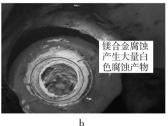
轮毂及尾减速器壳体固定螺栓孔腐蚀 Fig. 3 Wheel hub and bolt holes of TGB housing corrosion
